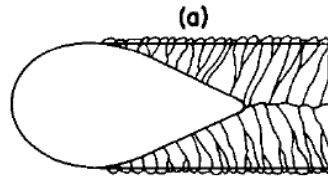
Crecimiento perpendicular a la frontera de grano del charco de soldadura
